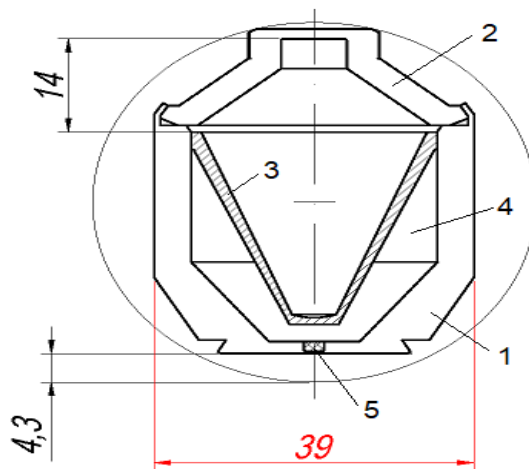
Конструкція заряду ЗКМ-54-У; 1 – корпус; 2 - кришка; 3 – лайнер; 4 – шашка ВР; 5 – проміжний детонатор
